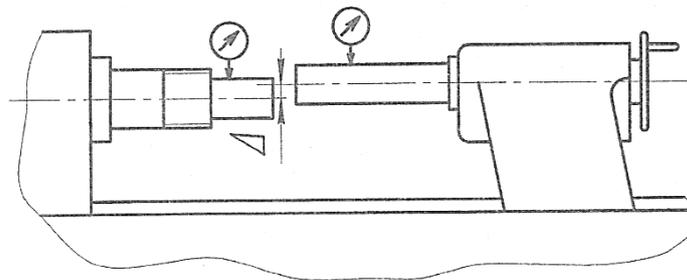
Схема установки индикатора для проверки одновысотности расположения осей отверстия шпинделя и пиноли
